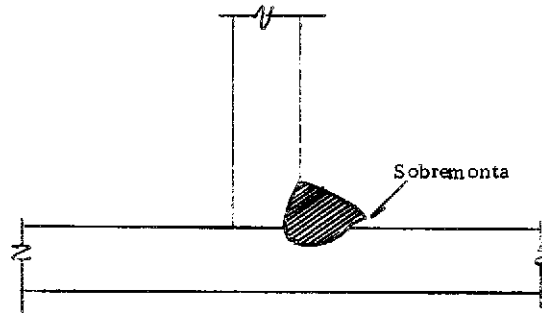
Filete de soldadura con sobremonta.
